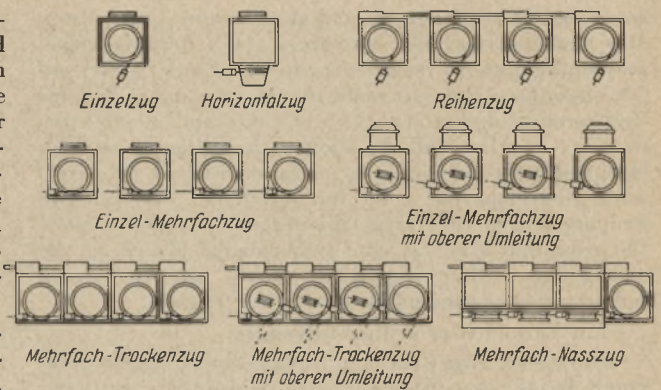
Bauformen und Bezeichnung der Drahtziehmaschinen.
